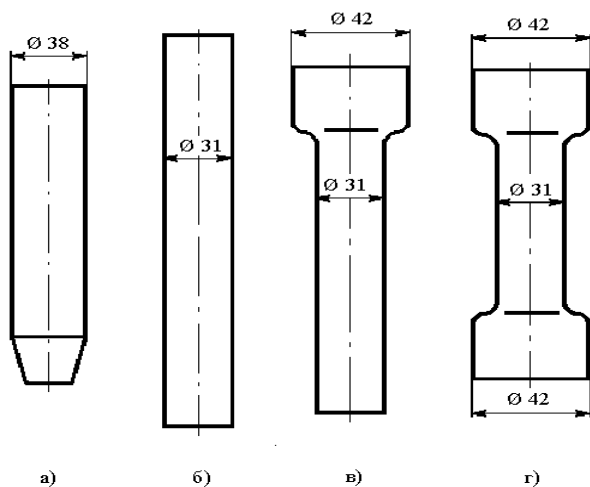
Технологические переходы формообразования заготовки рессоры: а) – заготовка, подготовленная к гидропрессованию; б) – экструдат (гидропрессованная заготовка); в) – высадка головки; г) – отштампованная заготовка.
